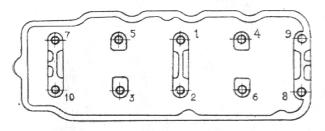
Reihenfolge beim Anzug der Muttern zur Befestigung des Zylinderkopfs am Motorblock für Motor 331.10
